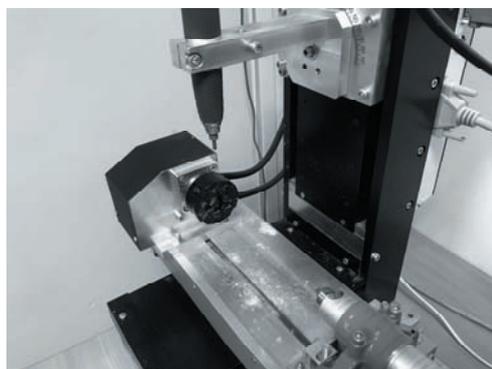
3D Фрезерный и гравировальный станок с ЧПУ с поворотной осью
